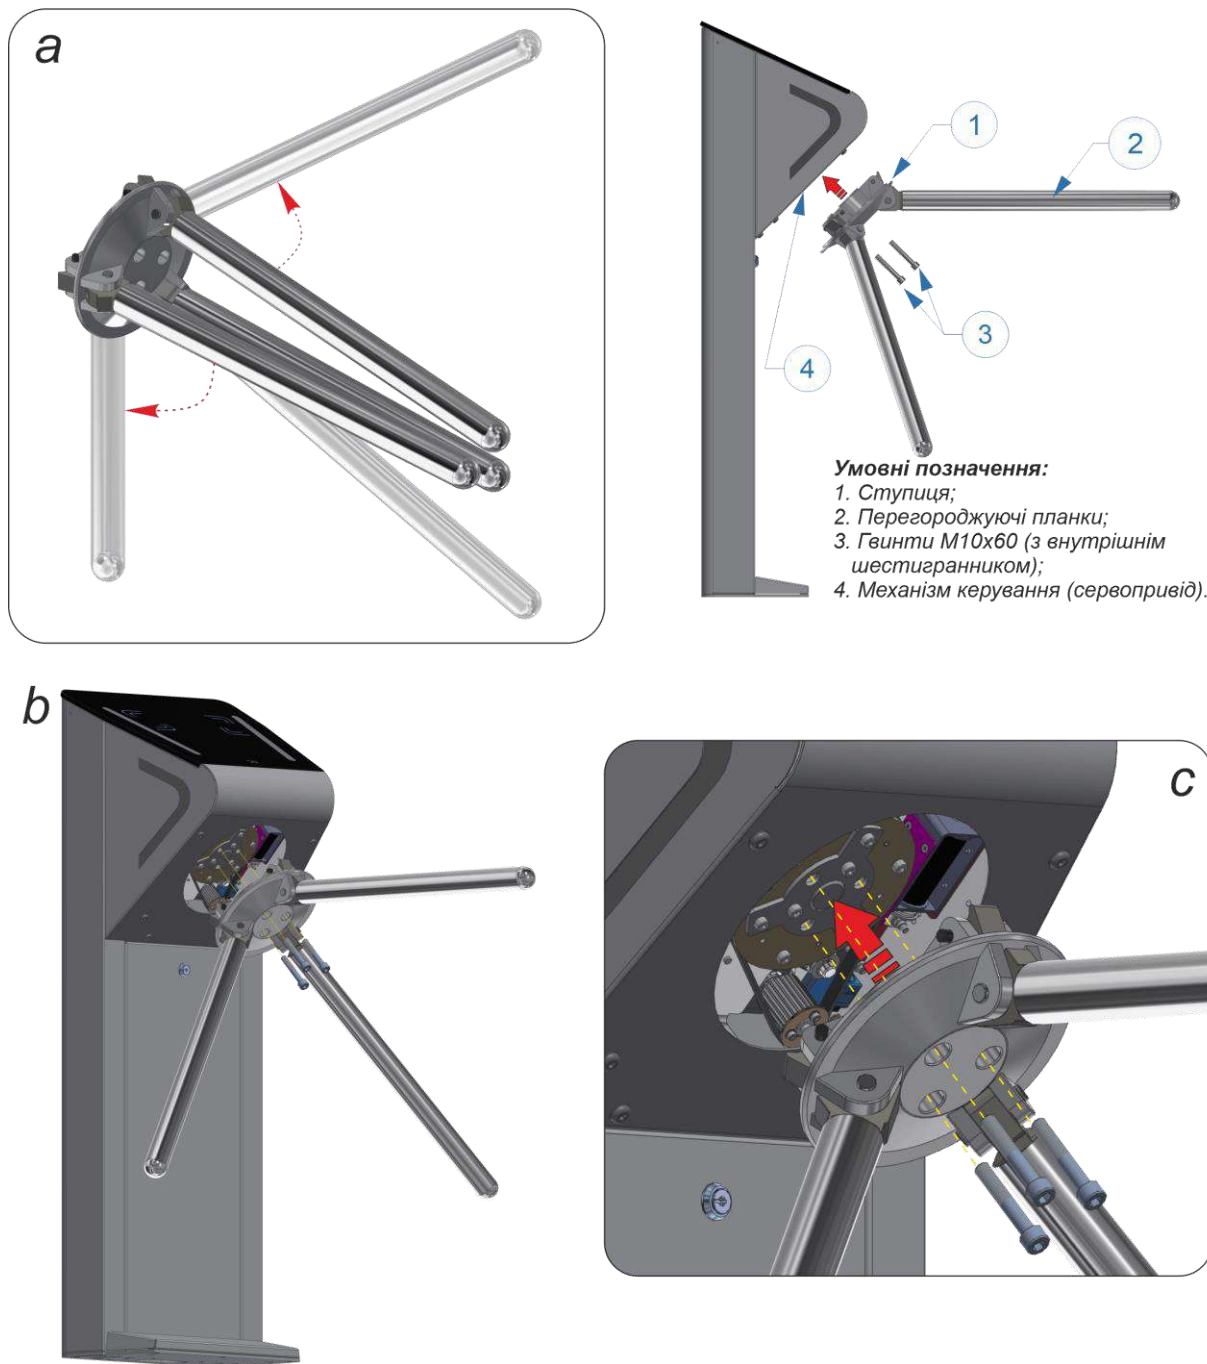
Встановлення ступиці з планками в корпус турнікету-триподу
